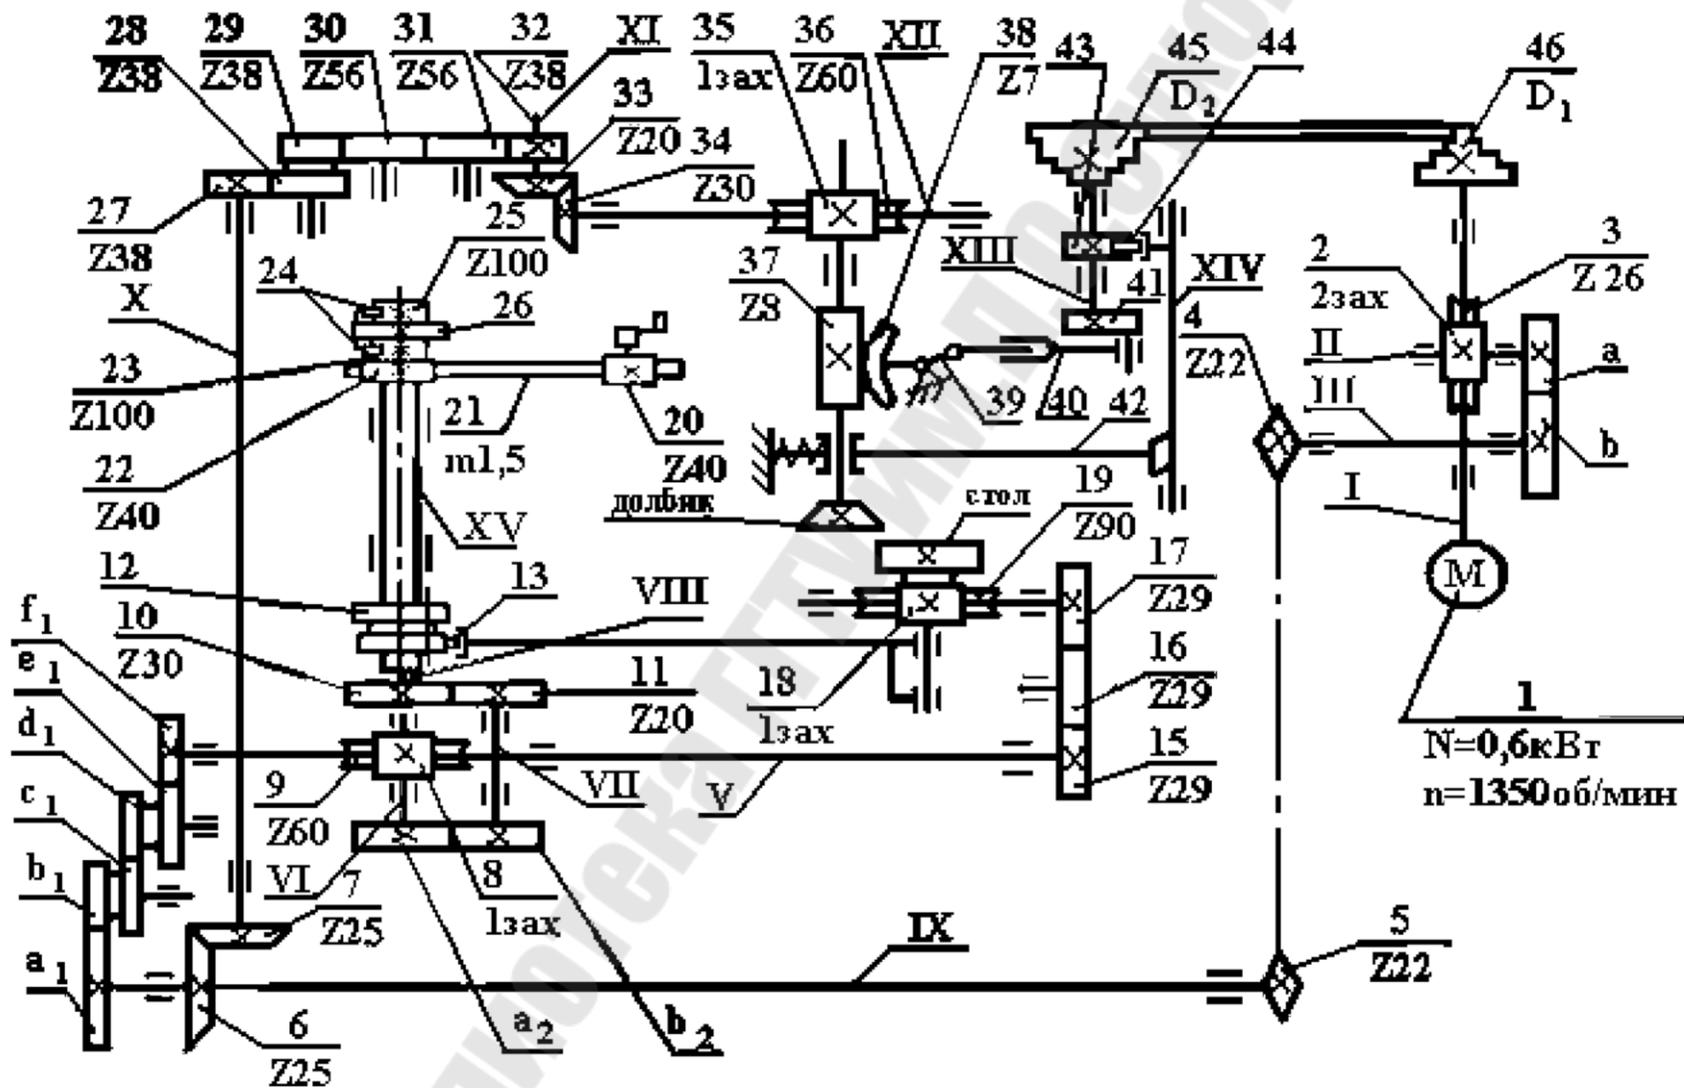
Кинематическая схема зубодолбежного станка
